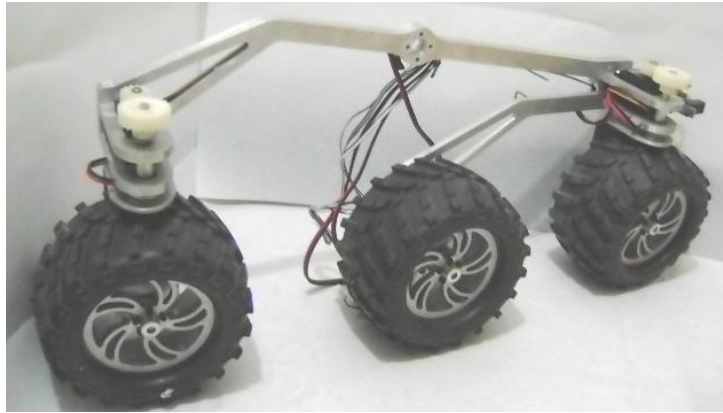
Ensamble subconjunto lado izquierdo del sistema de locomoción.
